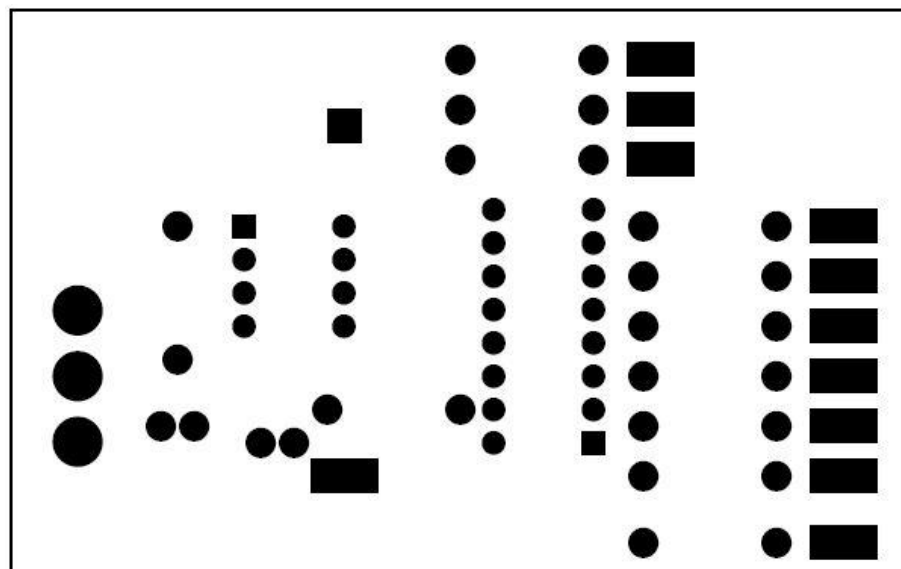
Fotolito máscaras de soldadura
